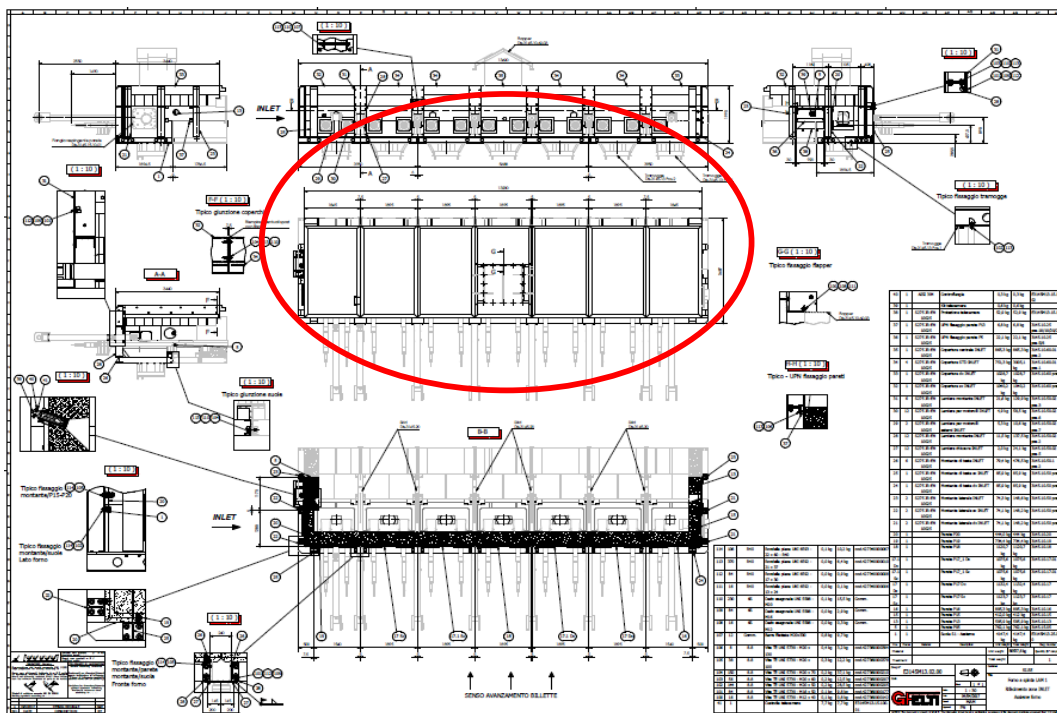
Plano Zona Vestíbulo (Módulos)
